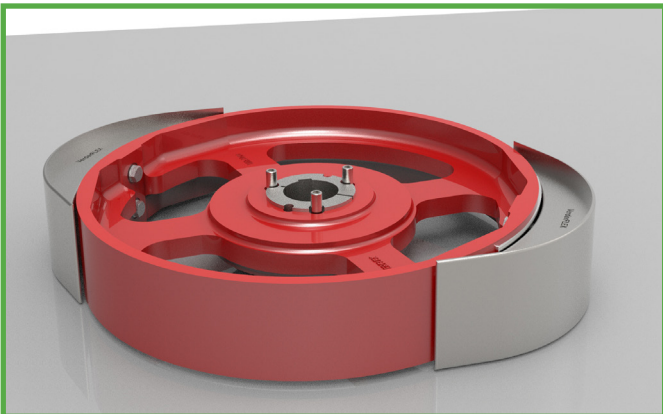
Montage des sabots du rotor sur le rotor (étape 2)
